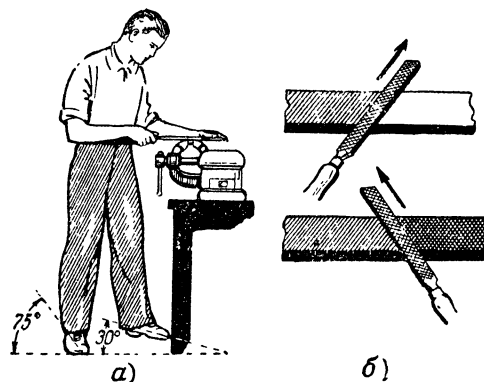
Крепление тисков к столу, рабочая «стойка» при работе напильником и опилование вперекрестку.
